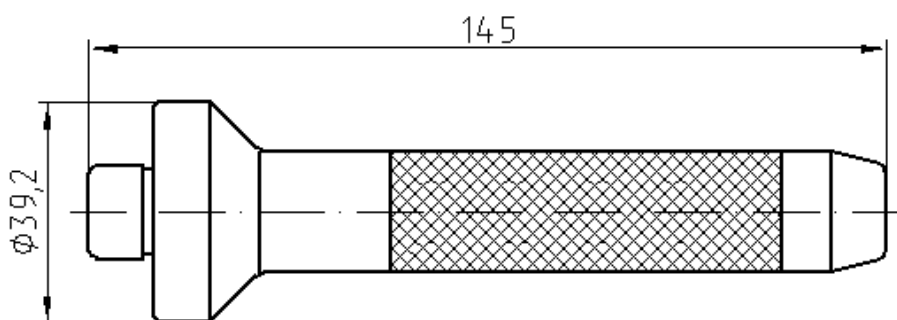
5-У-10897 – Оправка для запрессовки и выпрессовки подшипника первичного вала коробки передач
